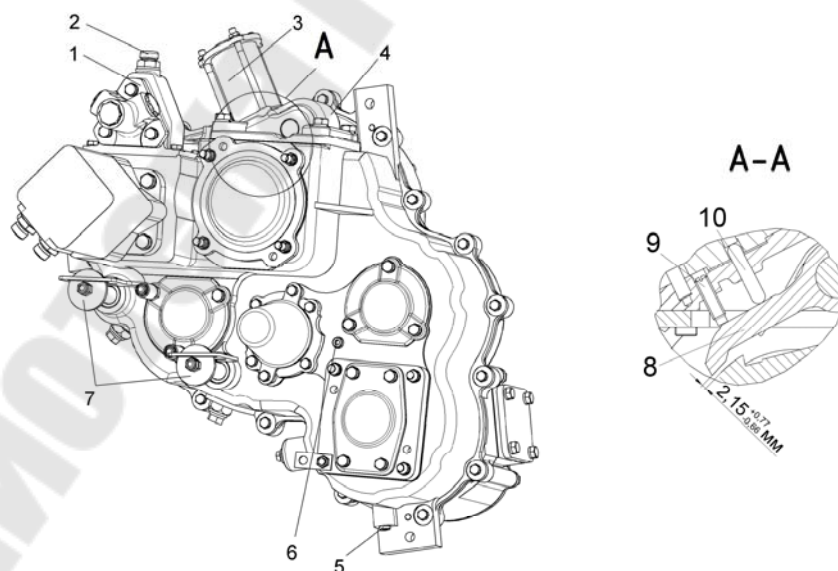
Коробка передач привода питающего аппарата (вид слева): 1 – механизм включения реверса; 2 – сапун; 3 – электромагнит; 4 – корпус; 5 – сливная пробка; 6 – контрольная пробка; 7 – шайбы; 8 – собачка; 9 – винт; 10 – толкатель
